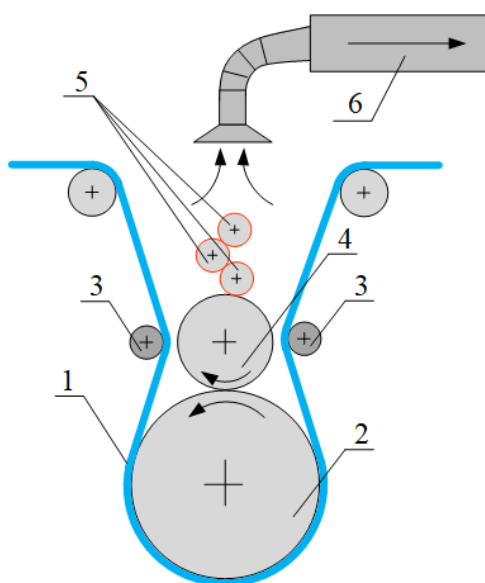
Схема узла машины для глубокой печати с дополнительными валами, прижимающими пленку к поверхности формного цилиндра:
